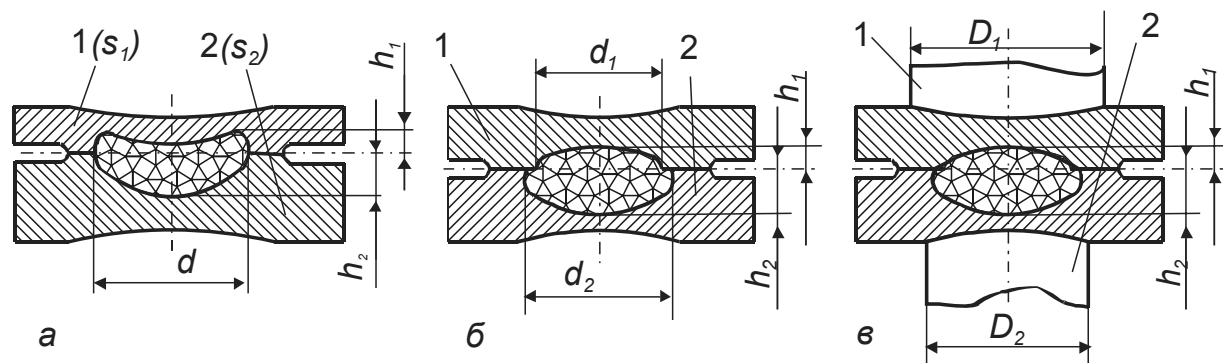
Вплив на формування зварної точки: а - різниці в товщинах деталей; б - їх питомого опору; в – діаметра зварювальних електродів
